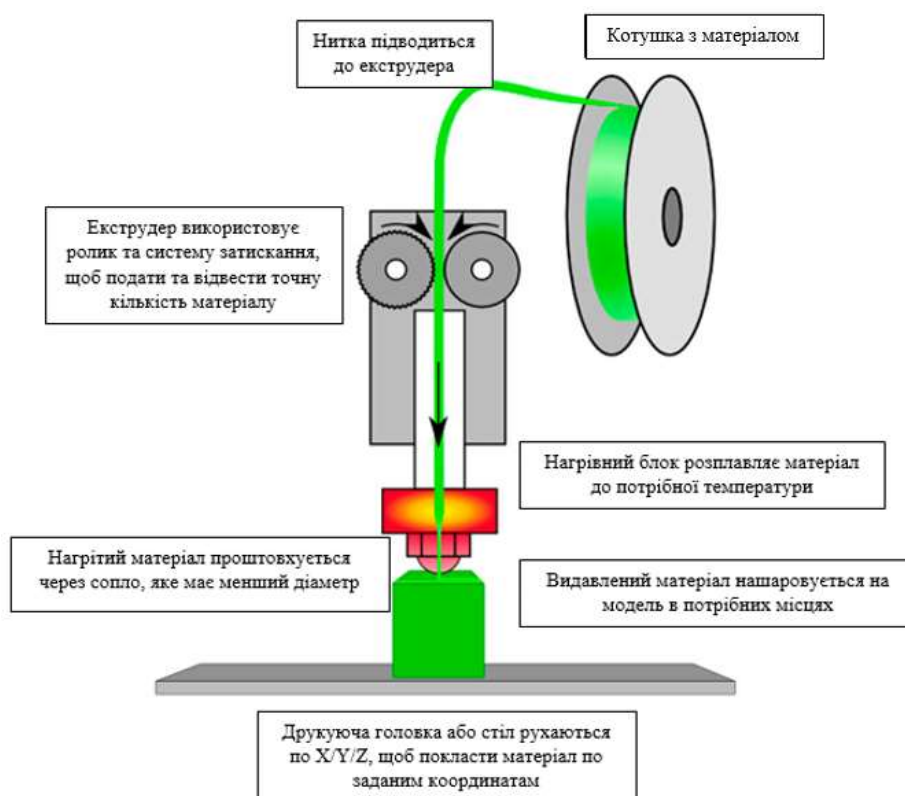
Схема пристрою 3D-принтера екструзивного типу
